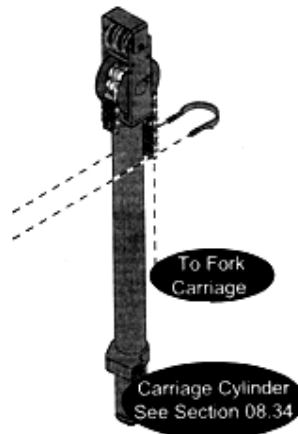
CILINDRO DE LEVANTE LIBRE
